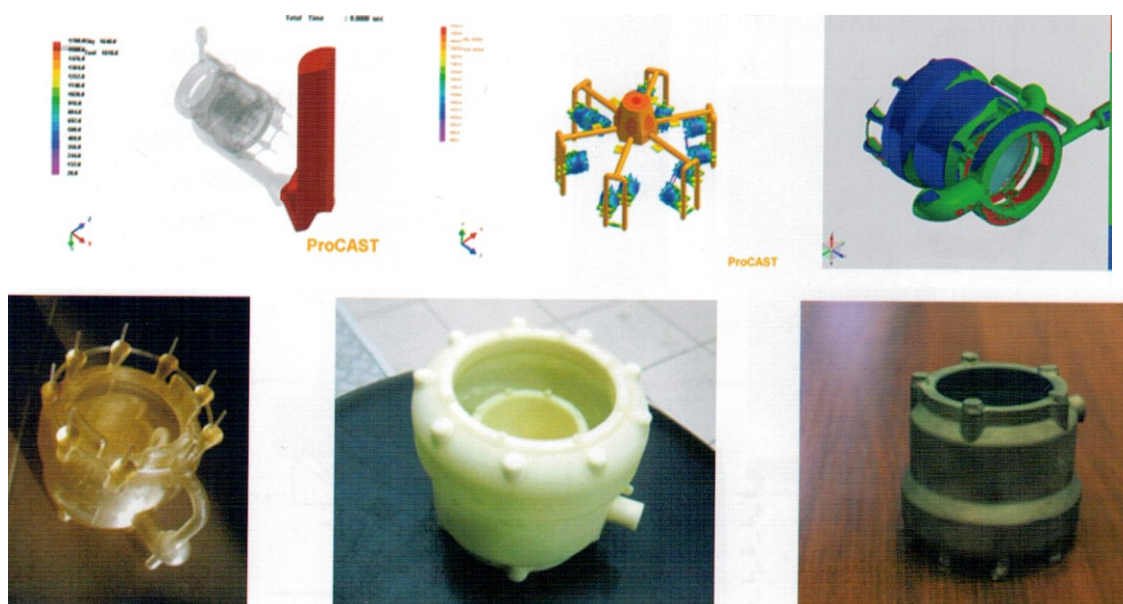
Этапы изготовления отливки «Корпус» из Ti-сплава
